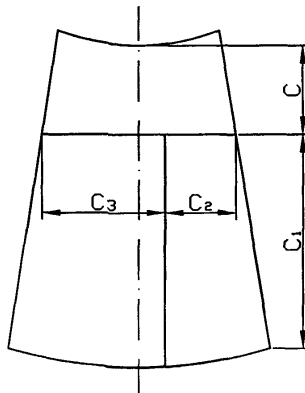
Расположение сварных швов при изготовлении лепестков штамповкой
